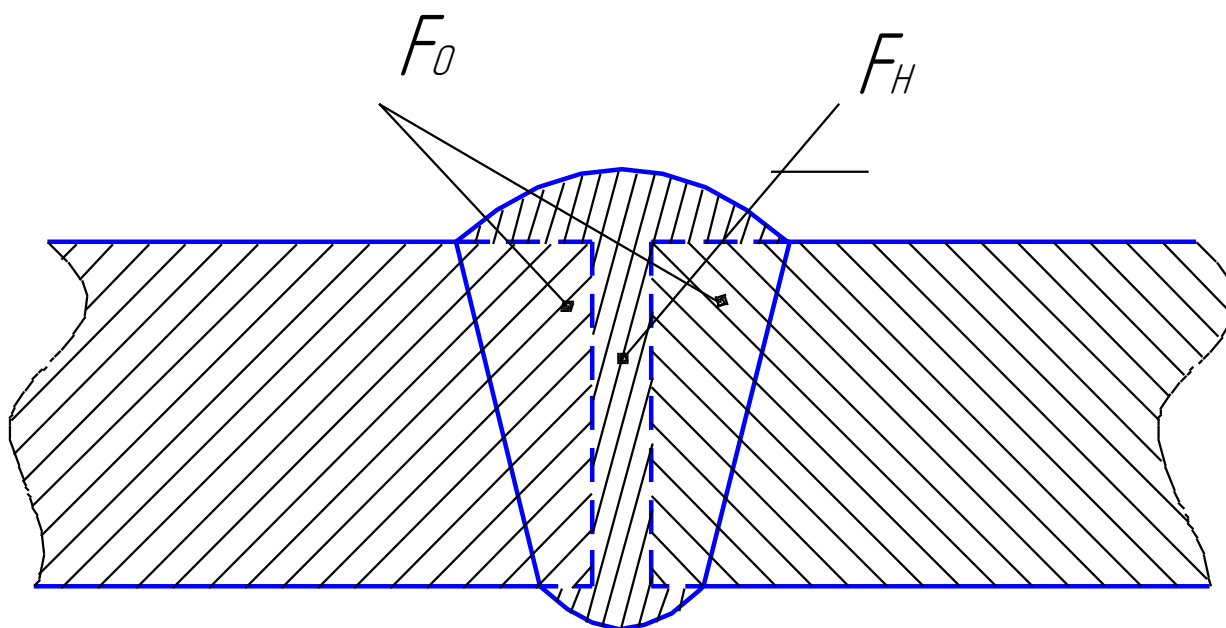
Схема поперечного перерізу стикового шва без розробки кромки
